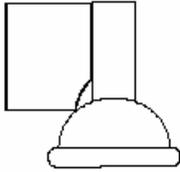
Das Werkzeug aus dem Werkstück zurückziehen.
